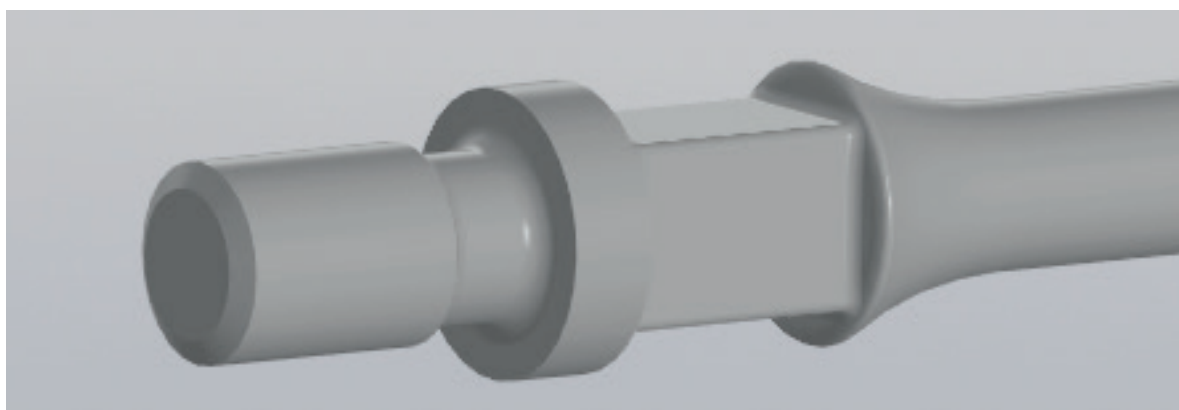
Общий вид соединения тела штанги с резьбовой головкой
